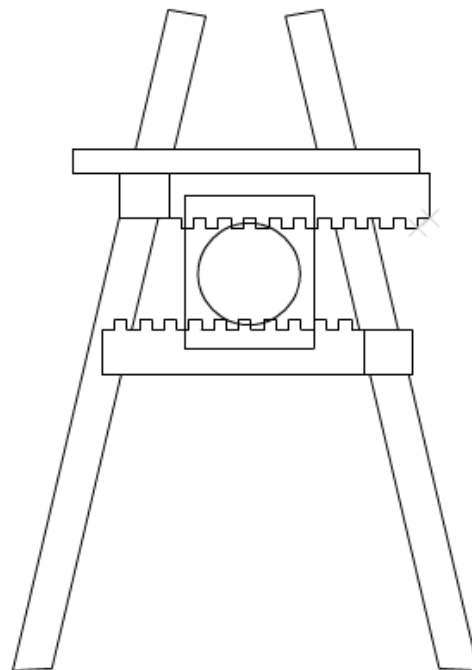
Diseño 2: sistema de cremalleras y engranaje
